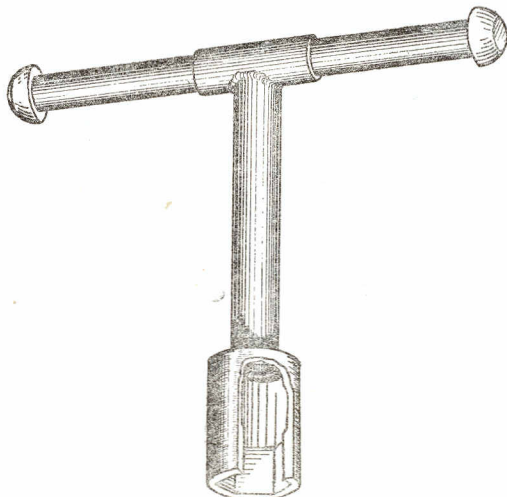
Ключ для гайки кулачковой шайбы синхронизатора.
